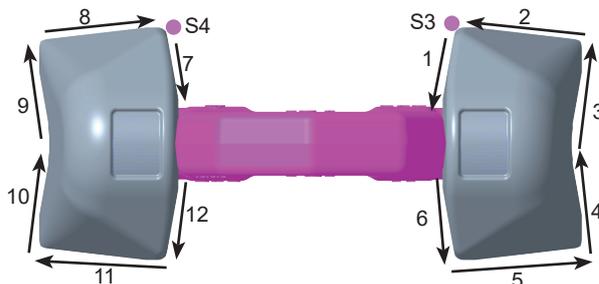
Ordre de soudure finitions (S = point de départ)
